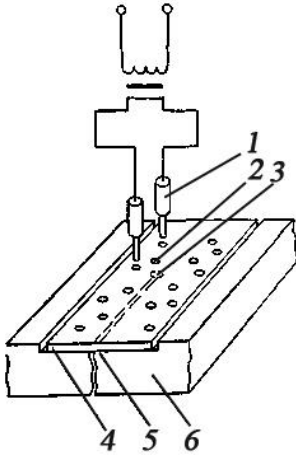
Схеми зароблювання тріщин клеєзварювальним способом:
